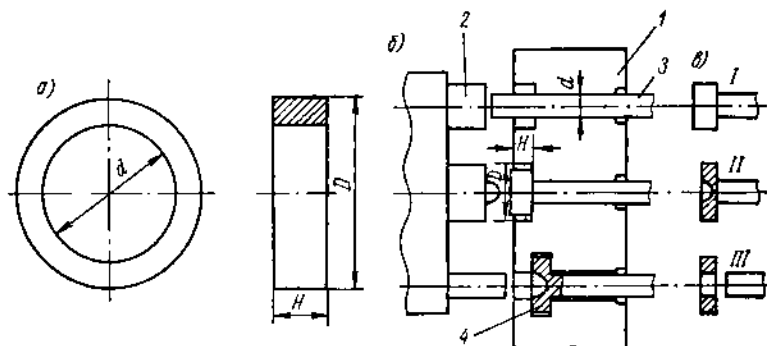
Штамповка кольца шарикового (роликового) подшипника: а — эскиз поковки; б — эскиз штампа; в — технологические переходы при штамповке
